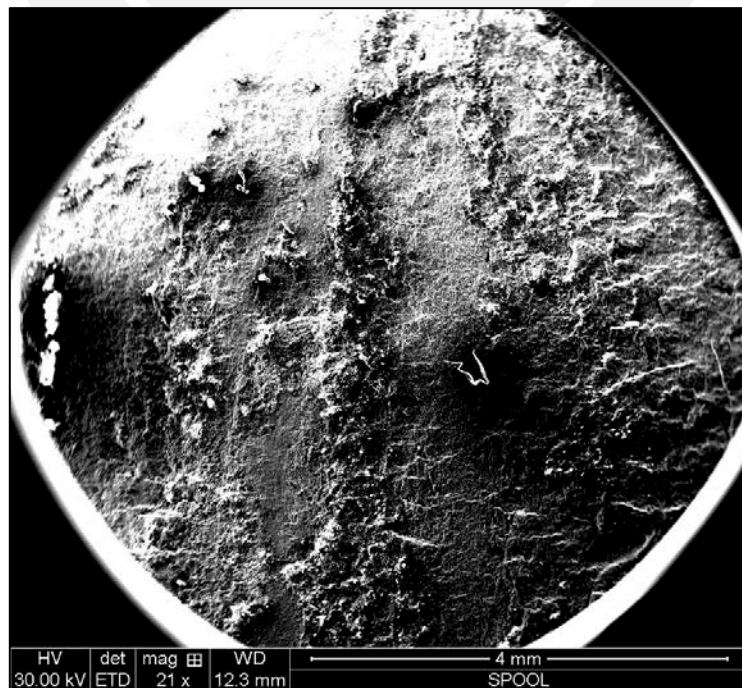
Se observa la superficie de fractura de la sección A-A de la probeta M3, con indicios del fenómeno de fatiga mecánica y fractura frágil.
